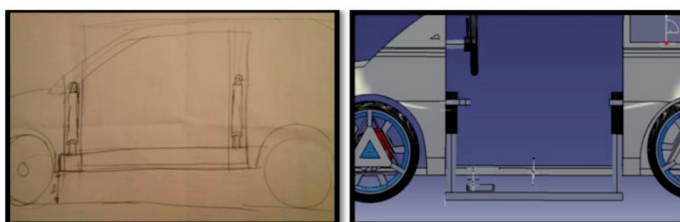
Boceto (izquierda) y diseño CAD (derecha) del mecanismo de elevación
